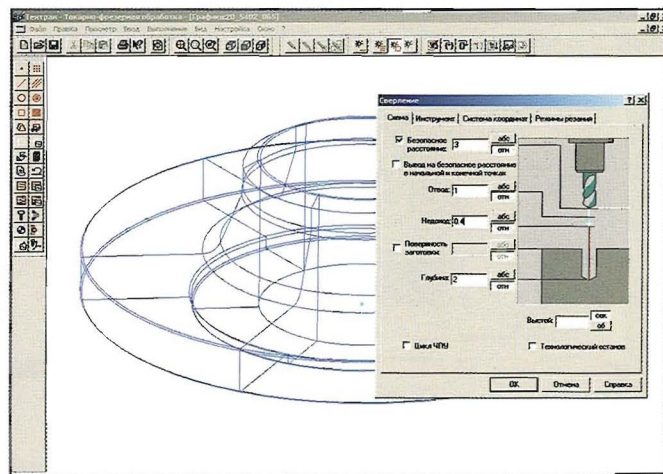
Фрезеруемые элементы строятся на основе геометрии заготовки на текущий момент
